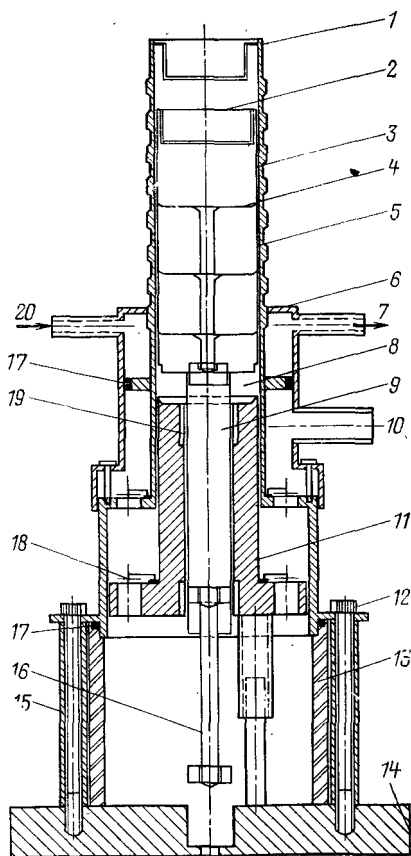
Двигатель Стирлинга свободнопоршневого типа (Била), работающий как воздушный компрессор.
